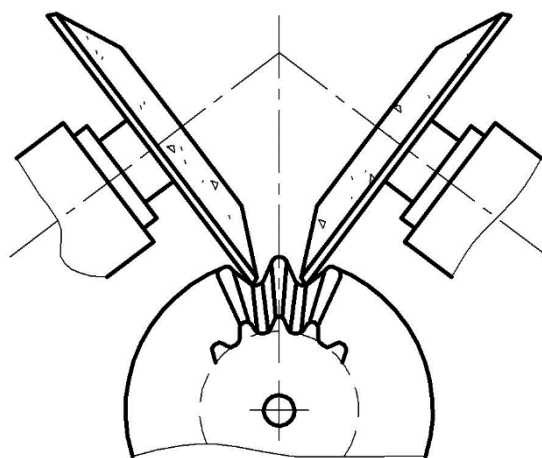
Зубошліфування конічного зубчастого колеса з прямим зубом
